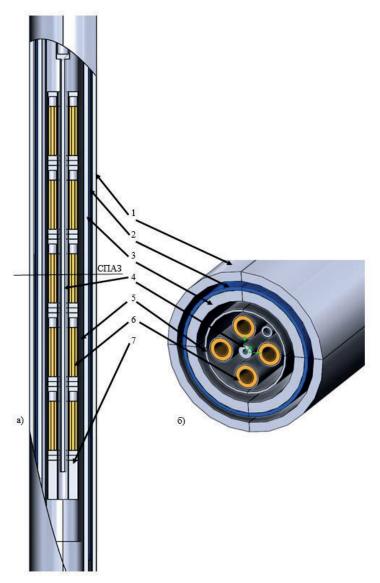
Конструкция ОУ: а — общий вид; б — поперечное сечение; 1 — наружный корпус; 2 — алюминиевая проставка; 3 — внутренний корпус; 4 — подвеска; 5 — разделитель потока; 6 — макеты твэлов; 7 — радиационные нагреватели
